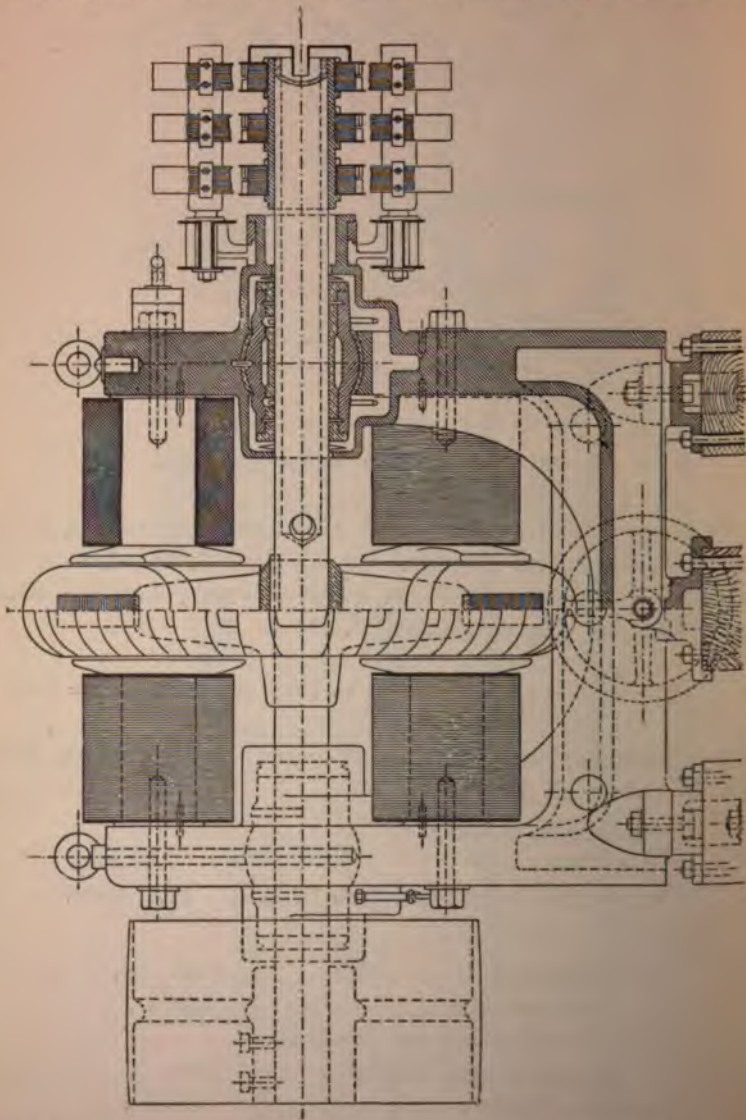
Brush Co.: Bogenlichtmaschine.
